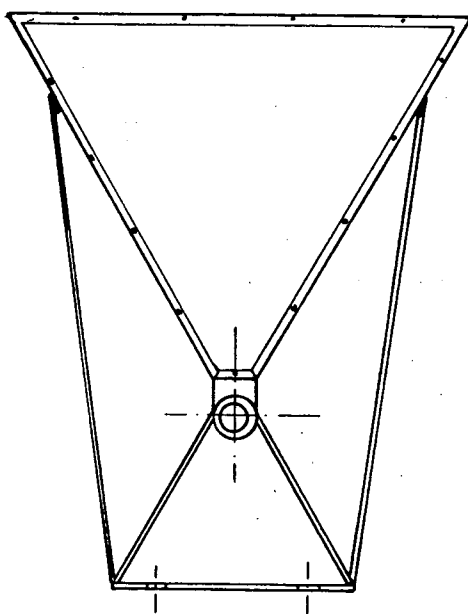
Conjunto adubador, mostrando detalhes de fixação no chassi da máquina.
